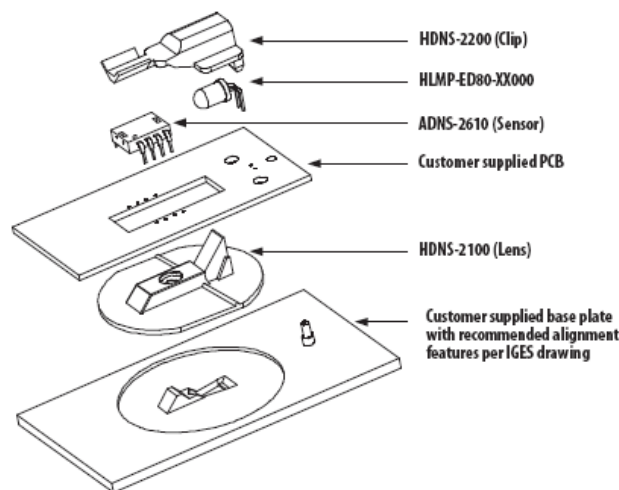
Vista explodida dos componentes de um rato ótico[24]
